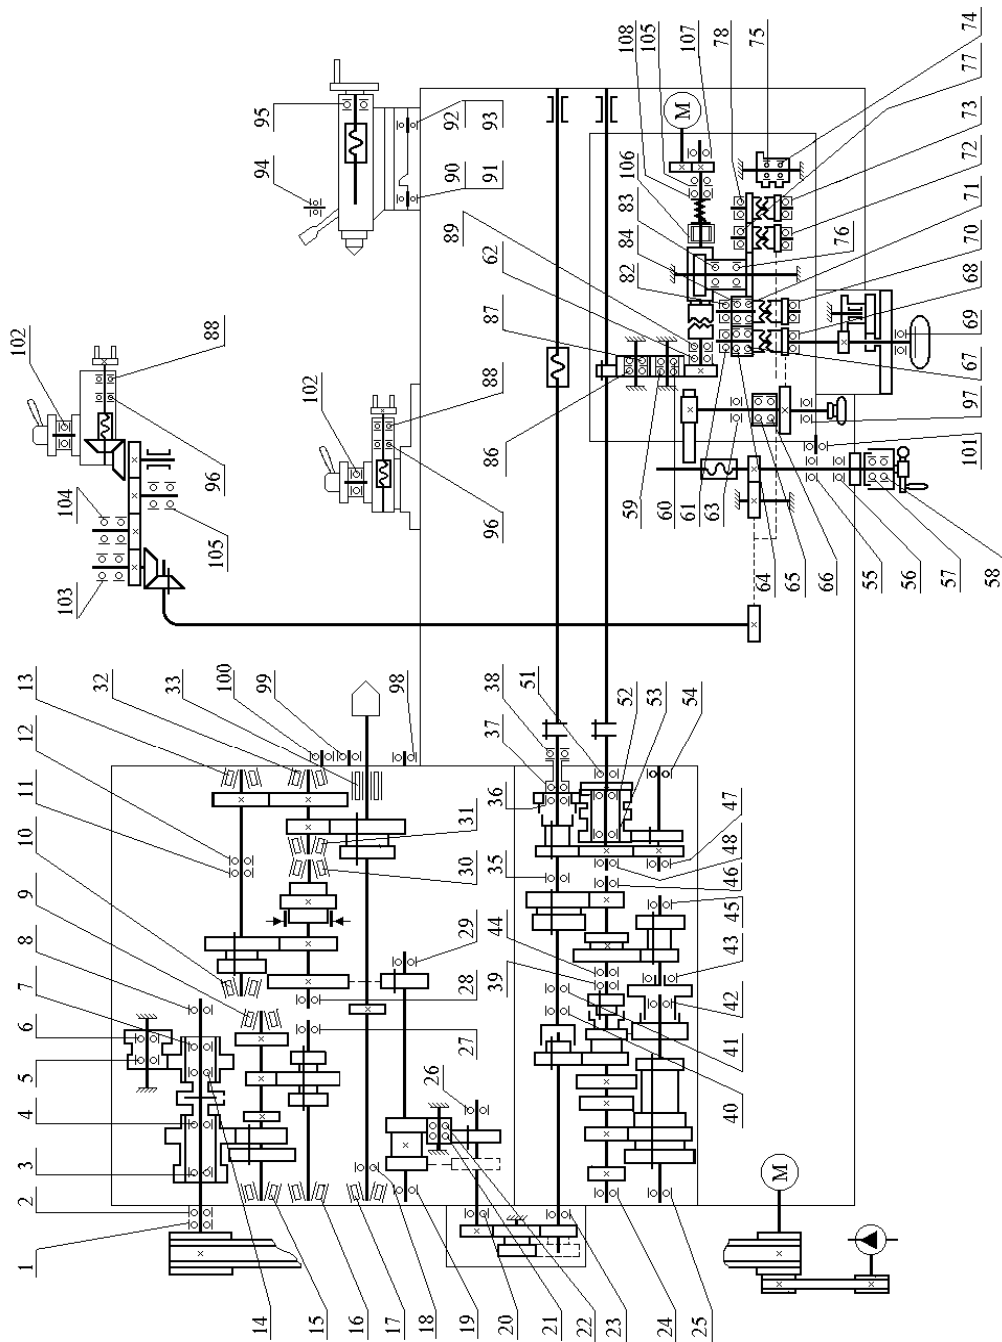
Схема расположения подшипников станка 16B20A, 1B62ГА, 1B625M (с механизированным приводом верхнего суппорта)
